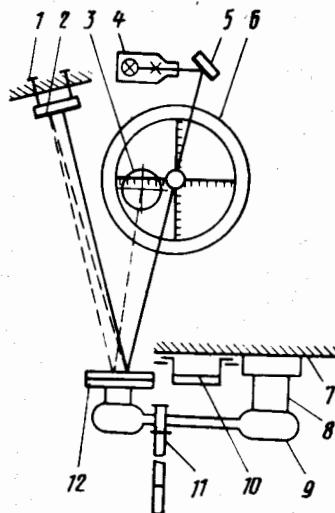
Принципиальная схема оптического прибора для проверки и правки шатунов
